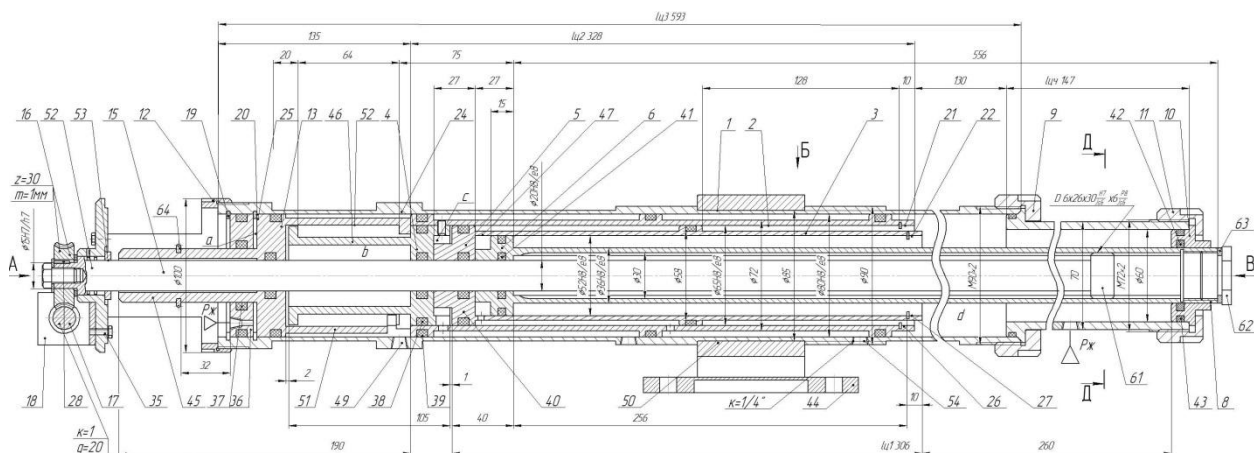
Телескопічний багатопозиційний привод поворотно-поступальної дії
